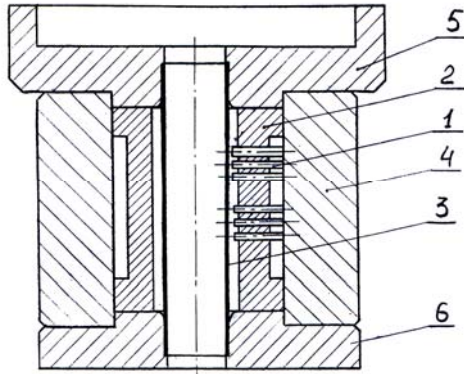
Схема оснастки для пробивки отверстий метанием трубчатой заготовки на неподвижно установленные пуансоны: 1 – пуансоны, 2 – пуансонодержатель, 3 – заготовка, 4 – бандаж, 5 – опорное кольцо, 6 – основание
